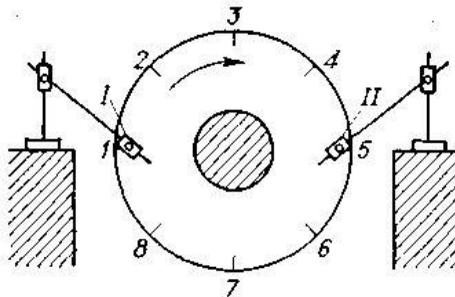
Схема проверки упорного диска на биение 2-е индикаторами 1 и 2
